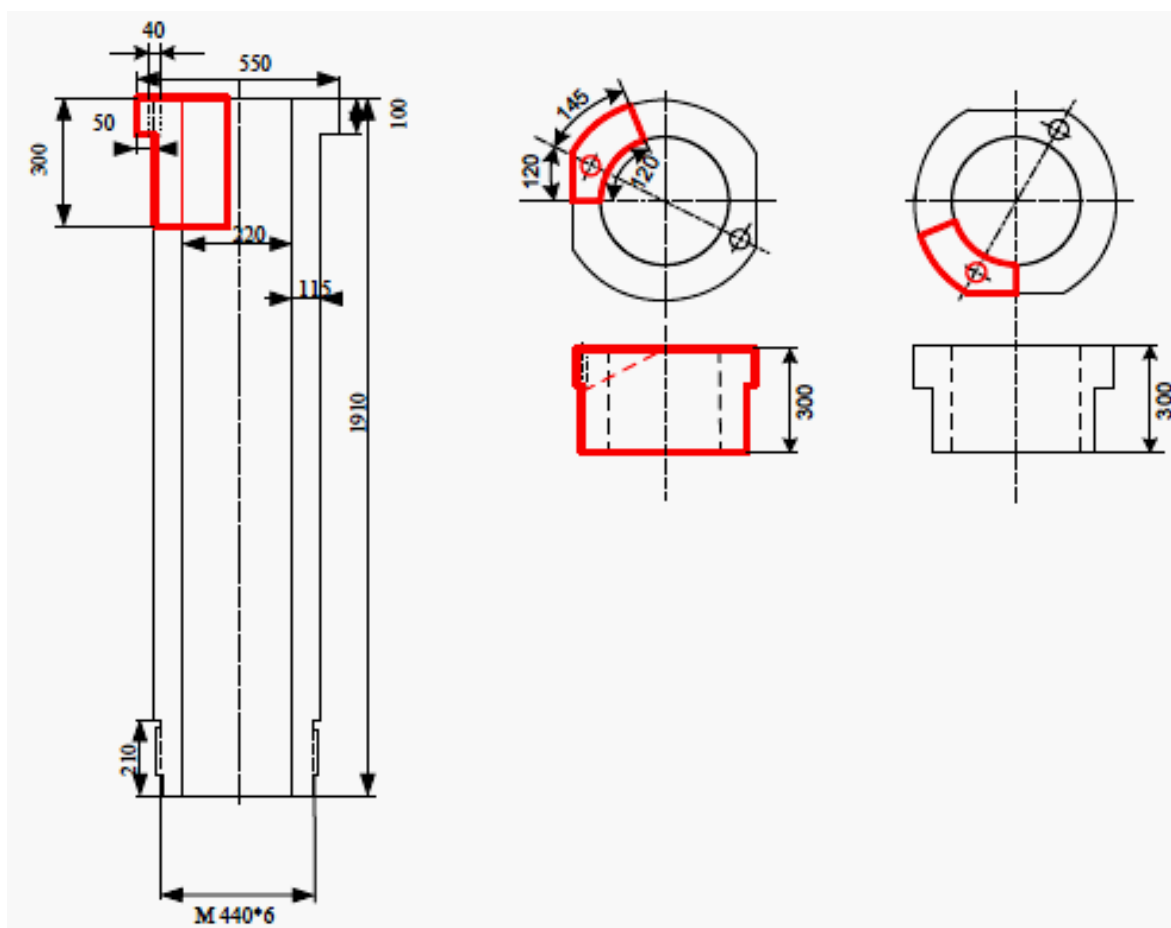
Схематичное изображение центральной цапфы и местоположения вырезки контрольного образца
